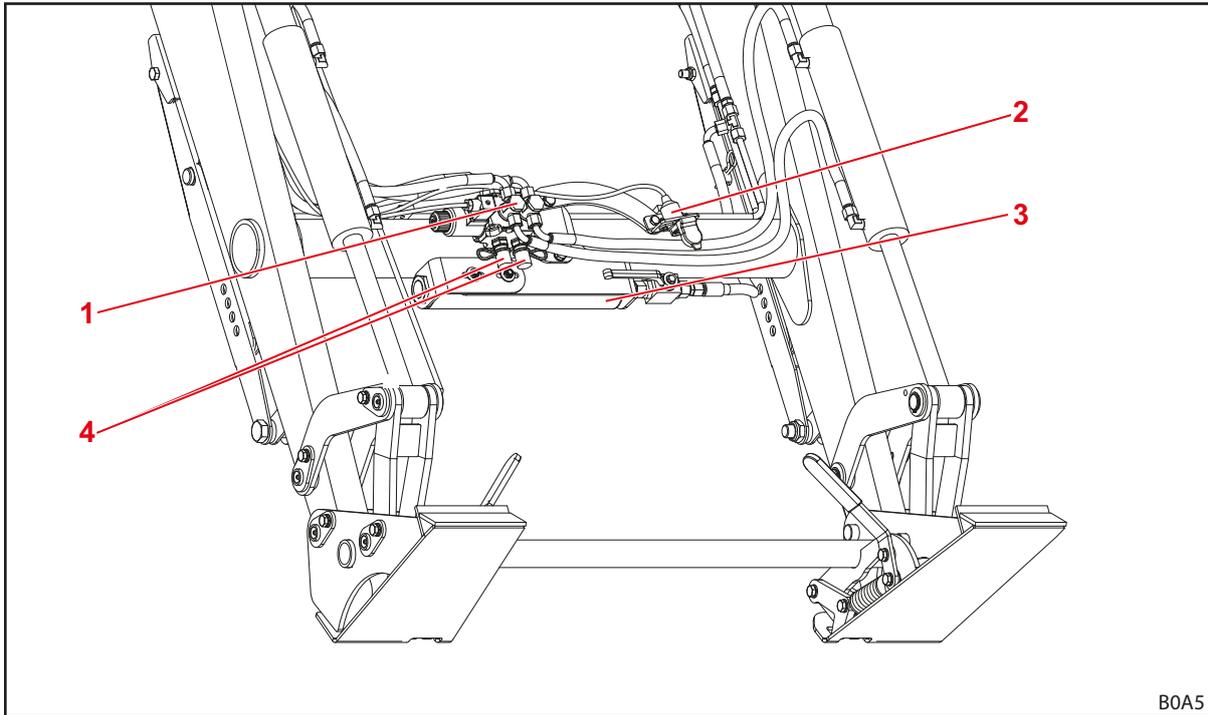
Equipamento adicional do carregador frontal L, H e P (figura de exemplo)
